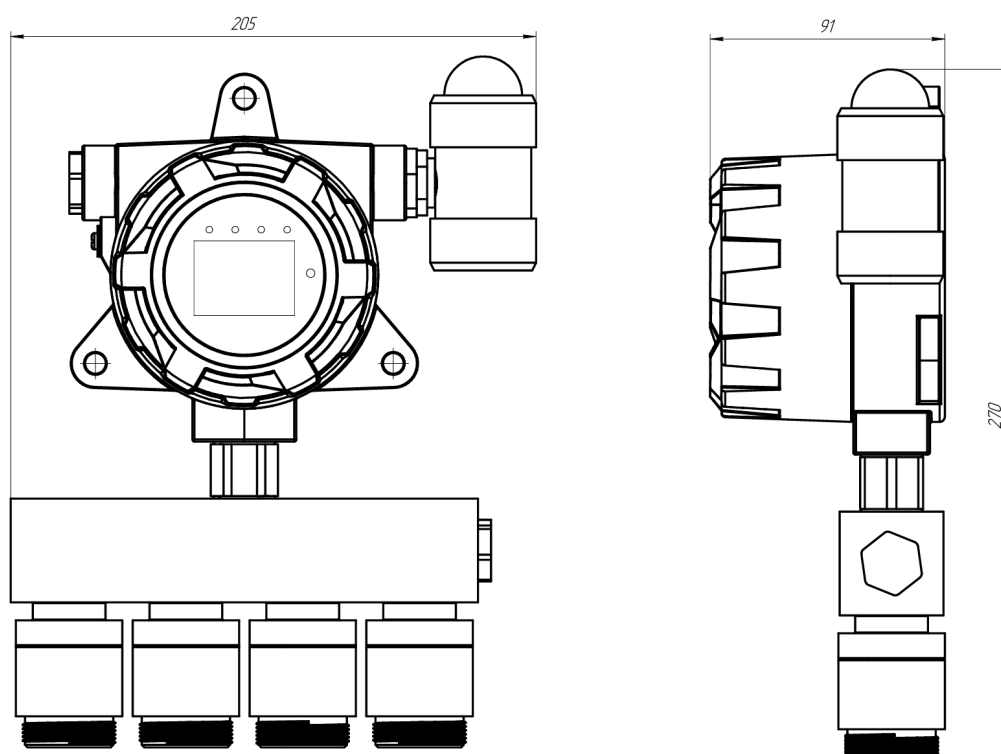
Габаритные размеры газоанализатора СИГМА-05-44
